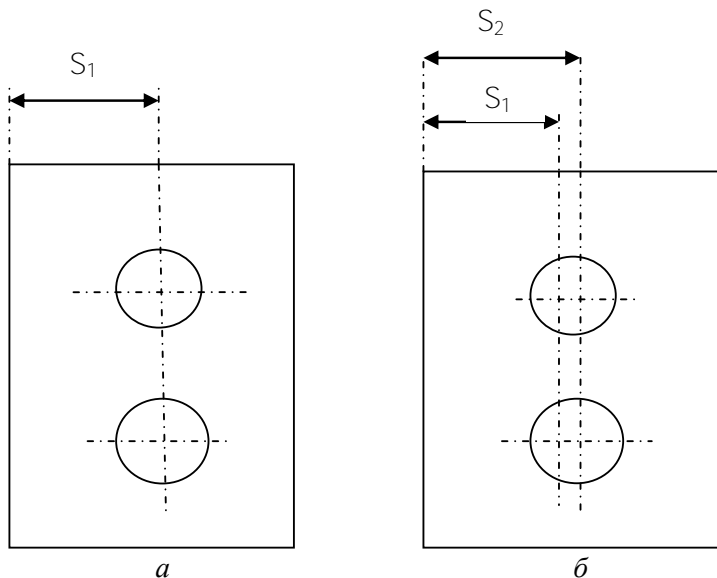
Размеры на чертеже детали (а) и схеме обработки (б)
